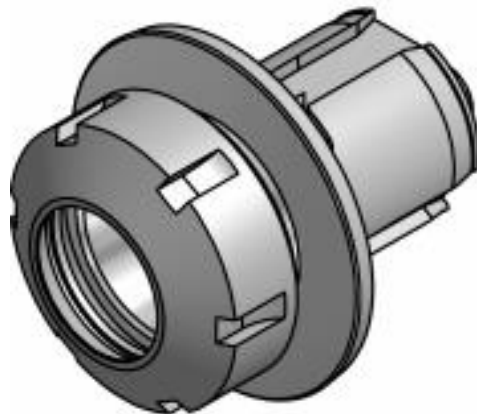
Цанговий патрон для фрезерної головки
